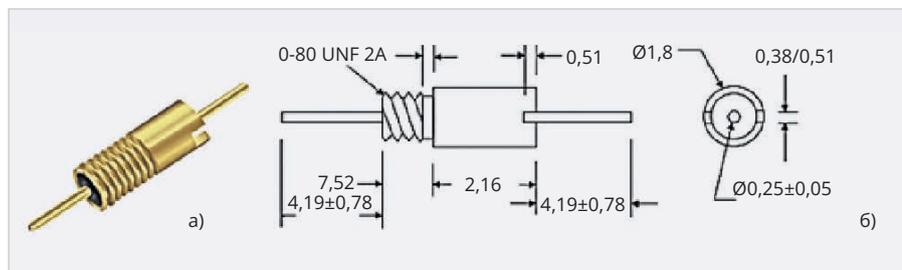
Фильтры для плотной упаковки изделий: внешний вид (а), конструкция (б)
